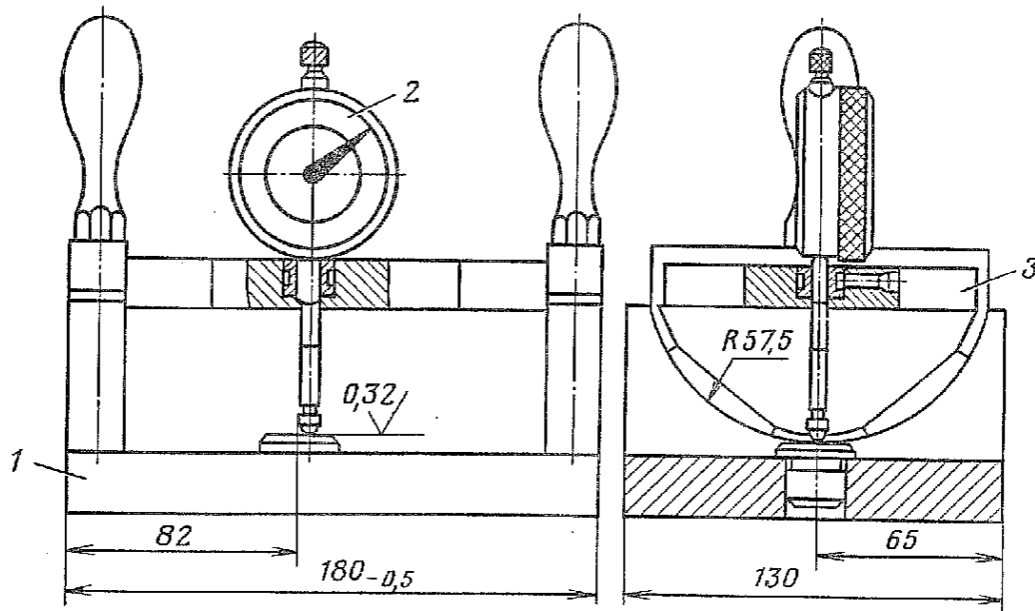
Контрольное приспособление для подбора толщины регулировочных прокладок ведущей шестерни главной передачи:
